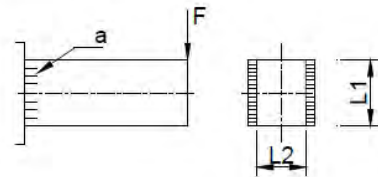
Soldadura sometida a una fuerza cortante y momento flector
